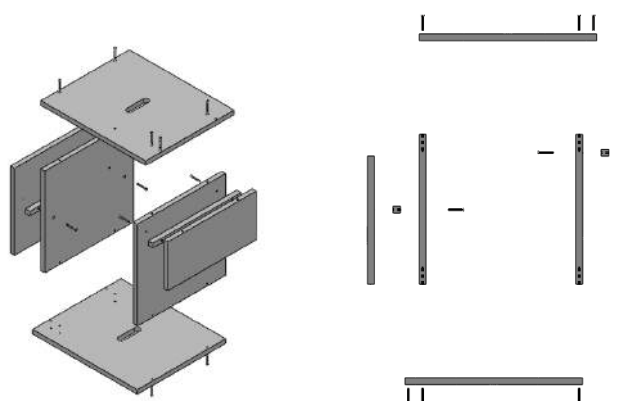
Vista explodida, perspectiva explodida do módulo.
